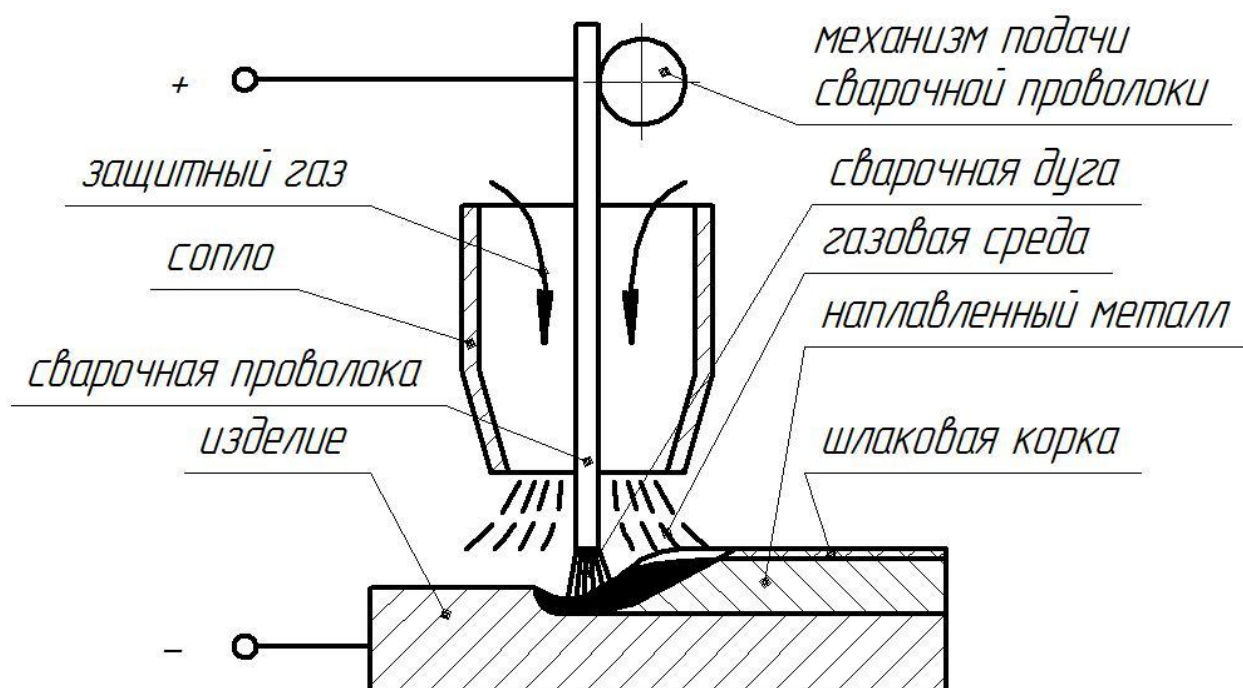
Схема установки для дуговой наплавки в углекислом газе
